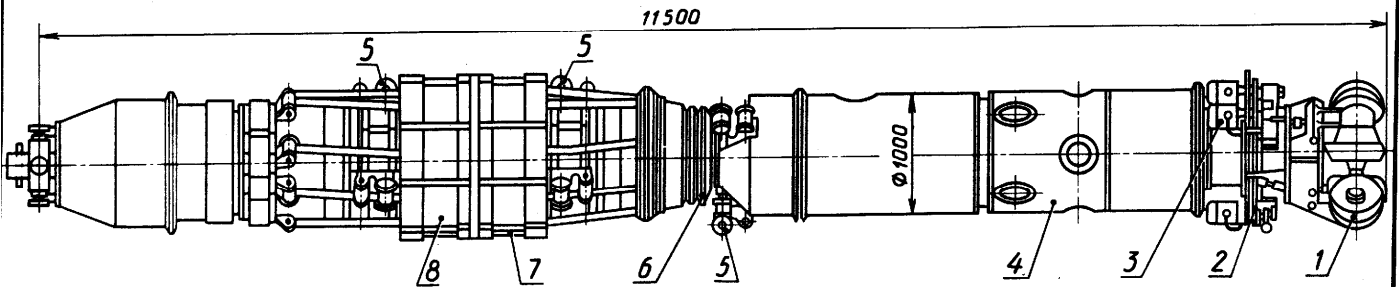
Внутритрубная установка «Север-1» для сборки и сварки стыков магистральных трубопроводов большого диаметра
